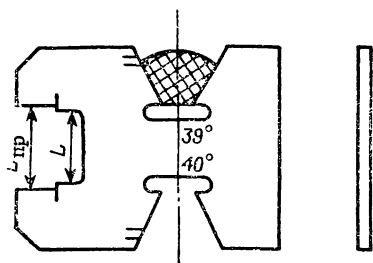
Шаблон для проверки поперечного сечения клинового ремня.
